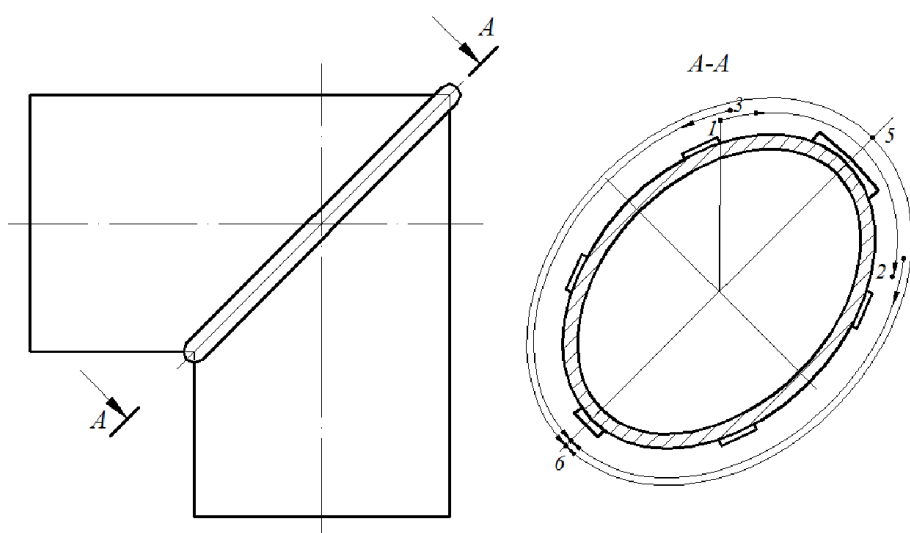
Схема сварки стыка труб: 1-2 первый слой; 3-4 второй слой; 5-6 третий слой
